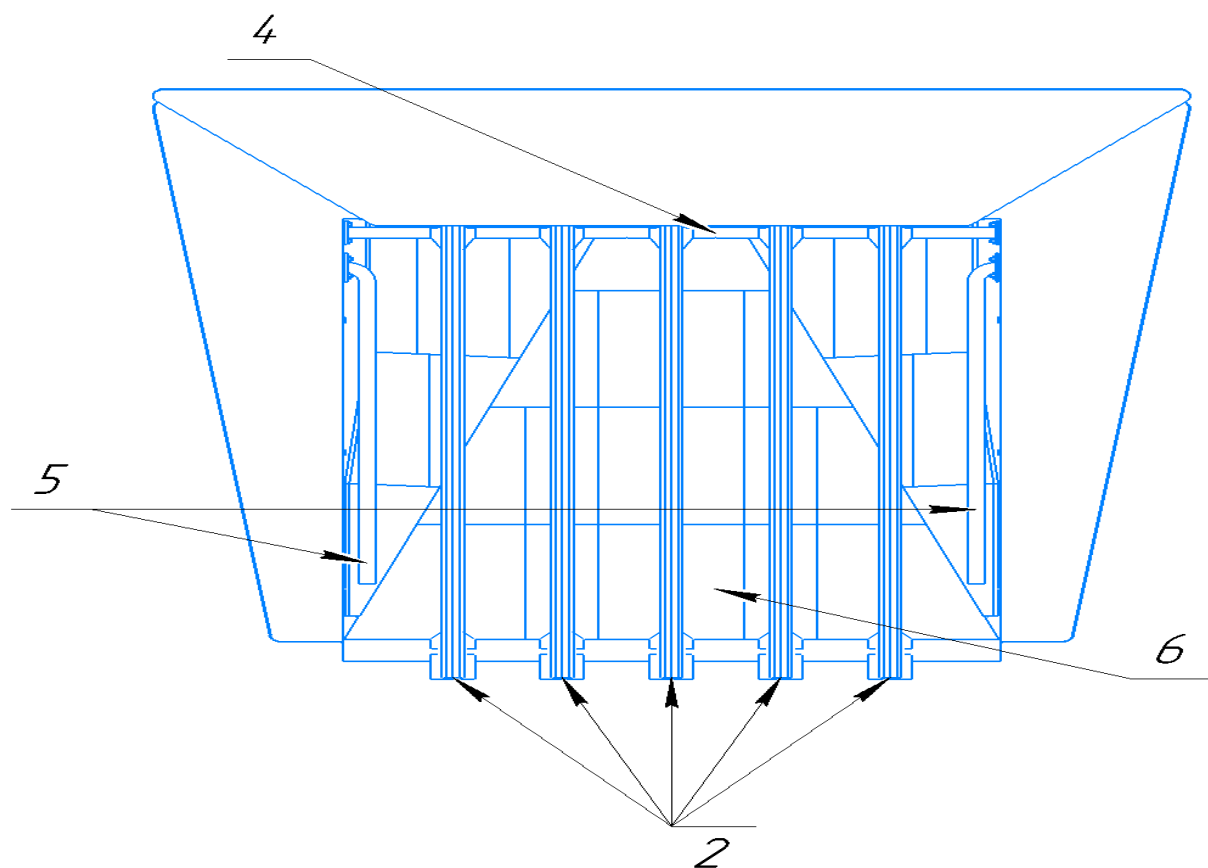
Модернизированный бункер промывочного прибора ПБШ-100 вид
